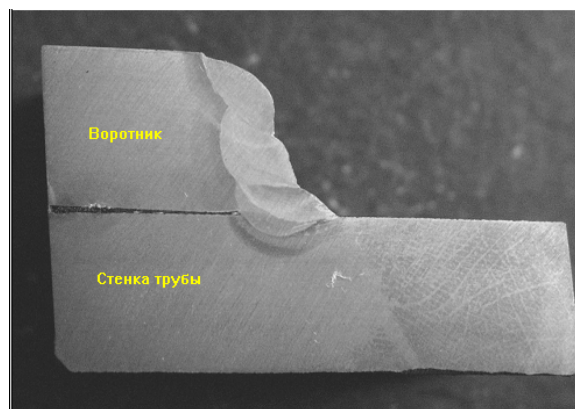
Макроструктура углового сварного шва “воротник-труба”
